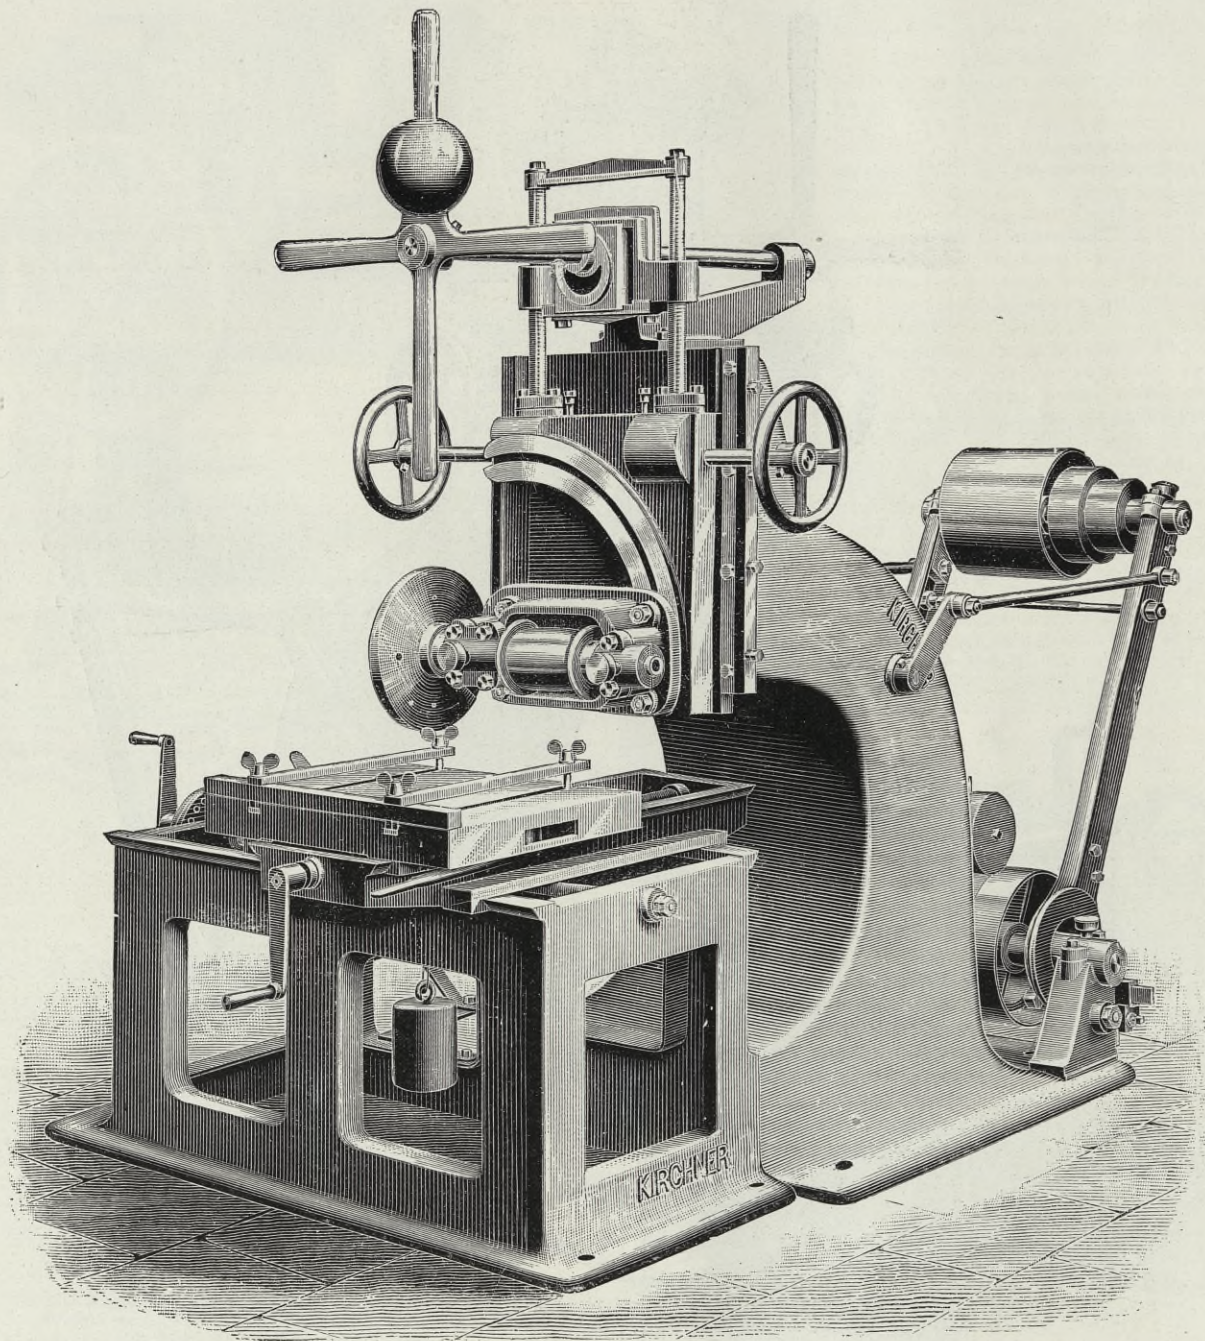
Hauptansicht der Fräsmaschine mit horizontaler Stellung der Frässpindel.
